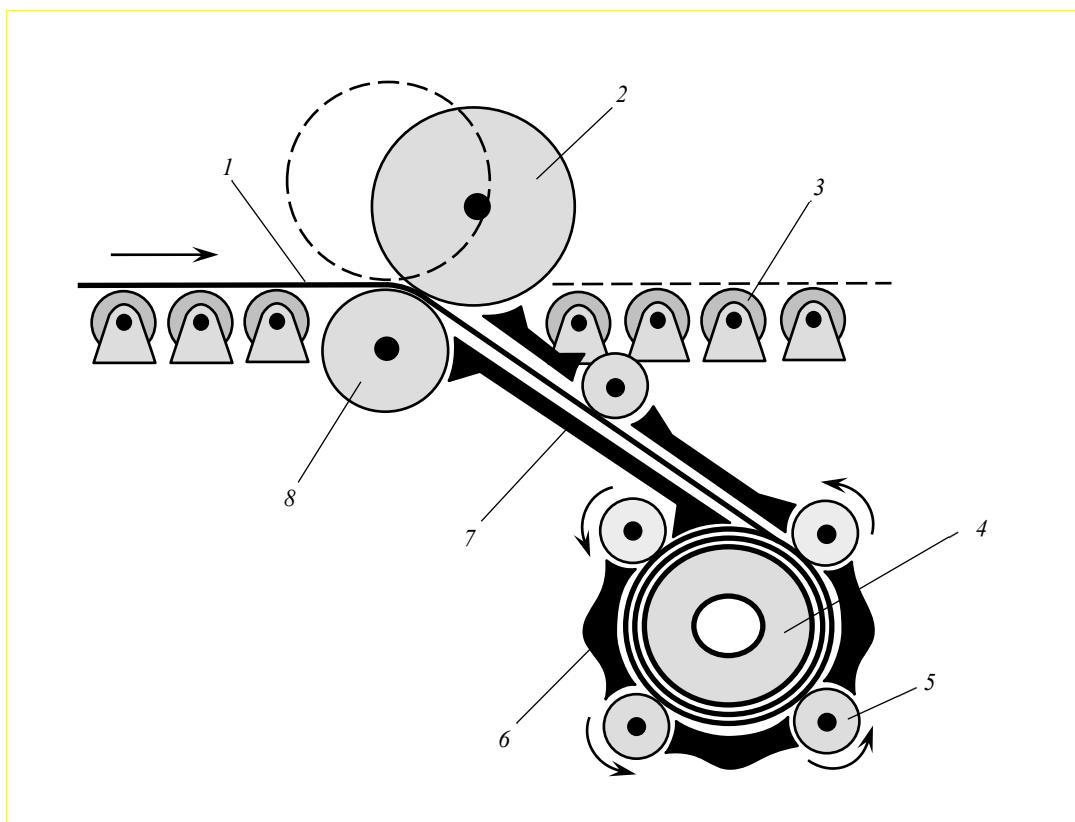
Схема ролико -барабанної моталки: 1 - Гаряча смуга; 2 , 8 - ролики, що подають; 3 - Рольганг; 4 - барабан; 5 - Формуючий ролик; 6 , 7 - Проведення
